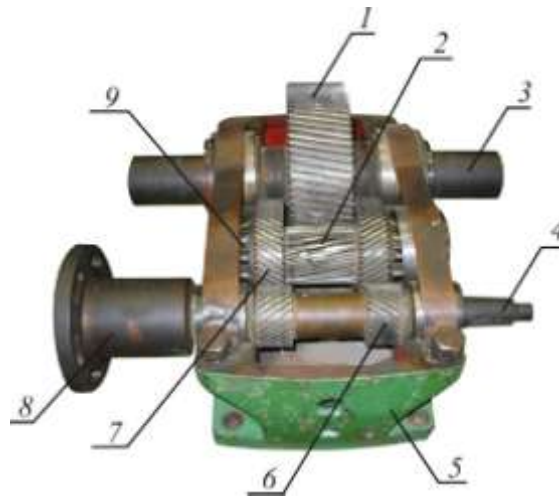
Редуктор двухступенчатый цилиндрический: 1, 7 — зубчатые колеса; 2, 6 — шестерни; 3, 4 — тихоходный и быстроходный валы; 5 — корпус; 8 — полумуфта; 9 — подшипник
